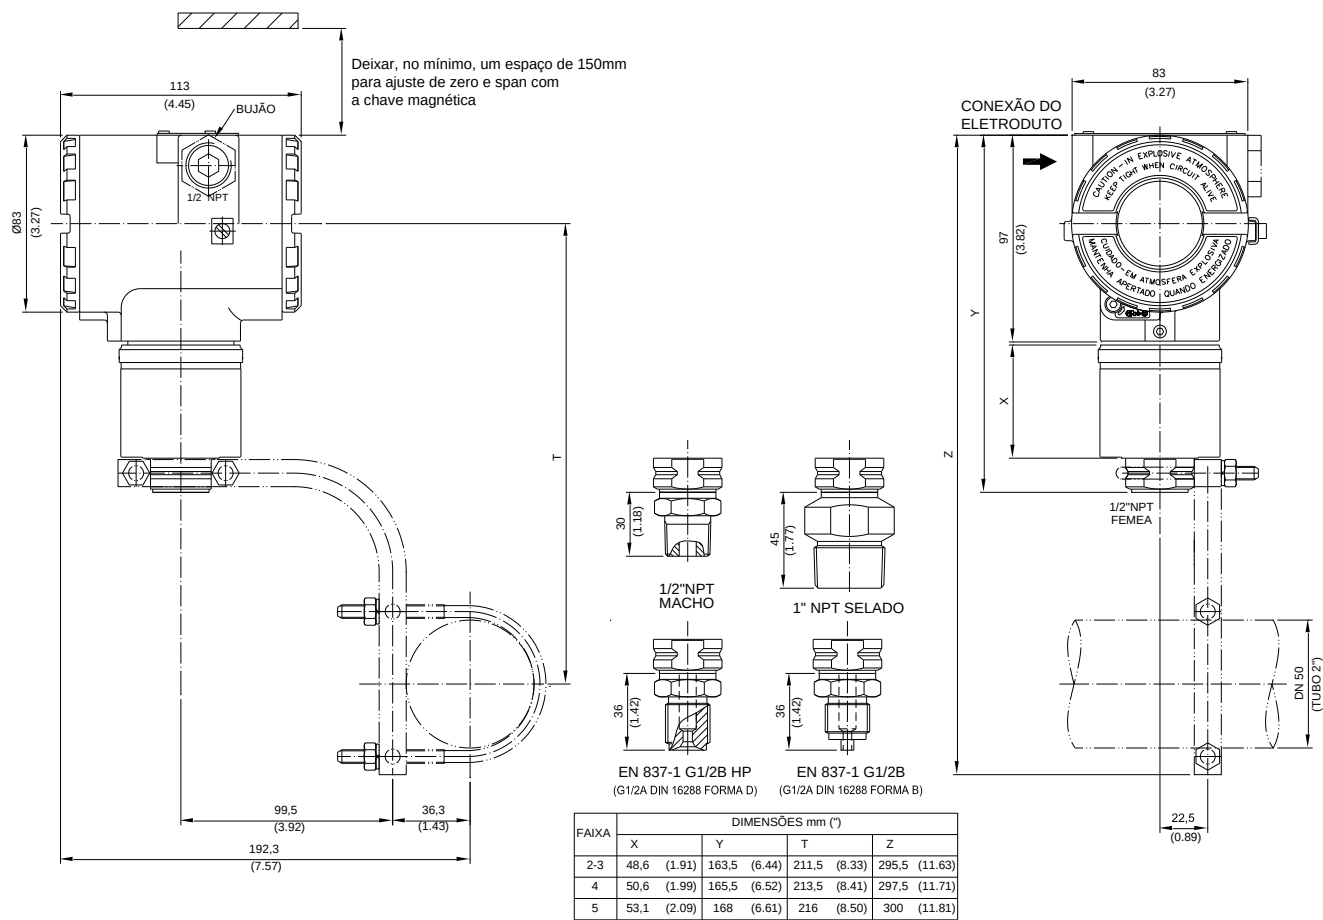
(a) - Desenho Dimensional de Montagem do LD290
